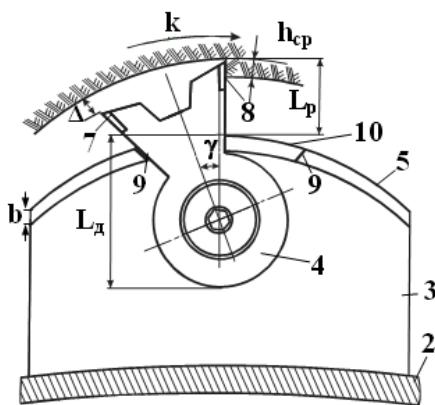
Принцип работы реверсивного двухлезвийного поворотного резца
